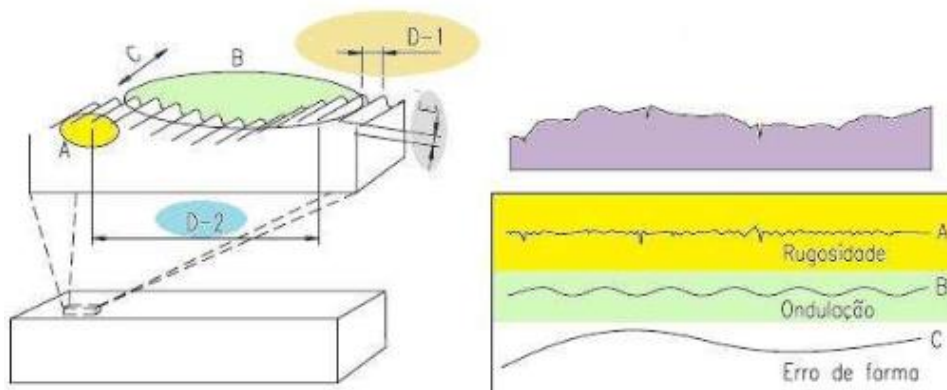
Elementos que fazem parte da composição de uma superfície (adaptado [12]).
